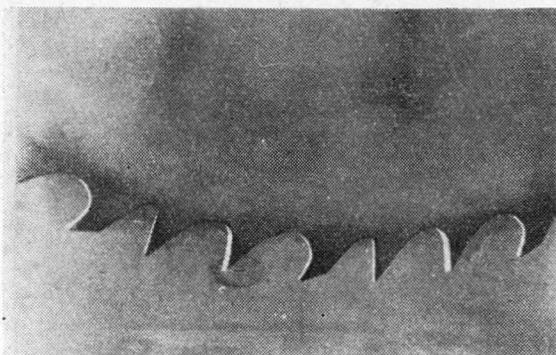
Зубчатый венец пилы со скалывающими зубьями.
